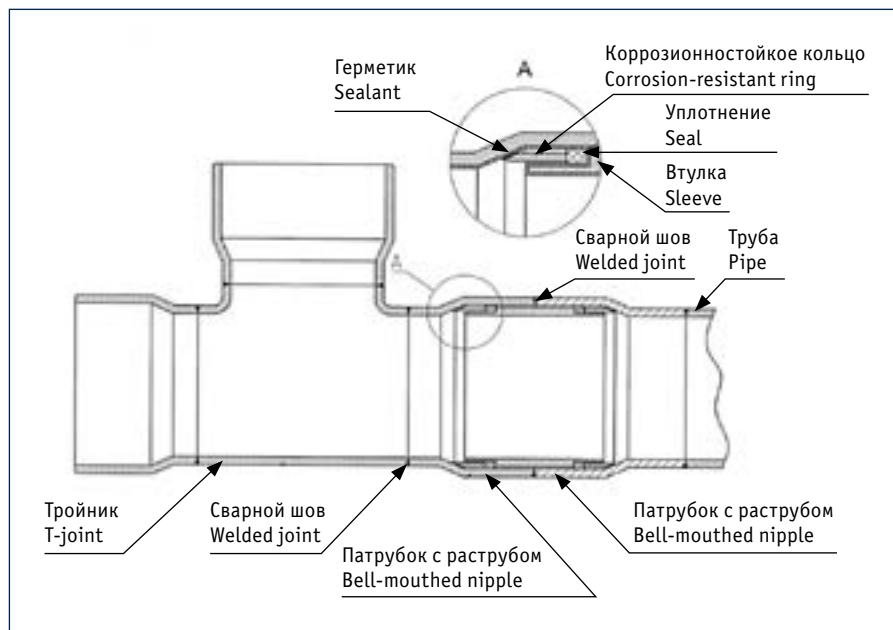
Внутренняя противокоррозионная раструбно-втулочная изоляция сварных соединений стальных элементов трубопроводов с внутренним эпоксидным покрытием
